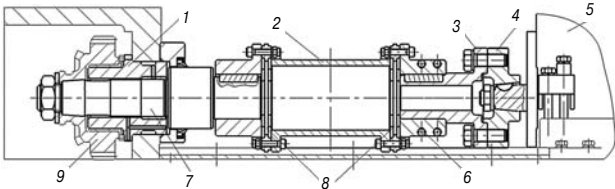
Общий вид модернизированной конструкции привода ТНВД:
